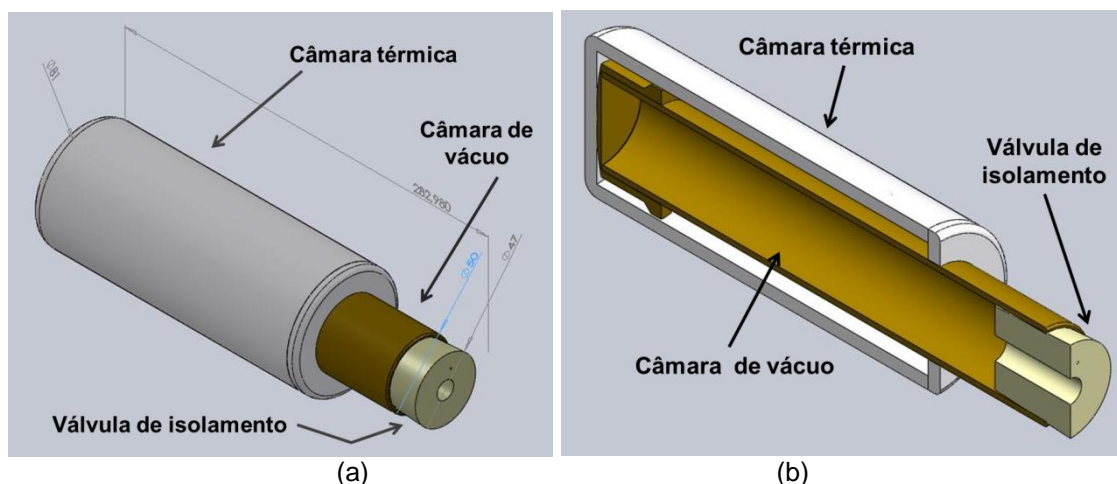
4. Câmaras montadas em (a). Corte longitudinal das câmaras (b).
